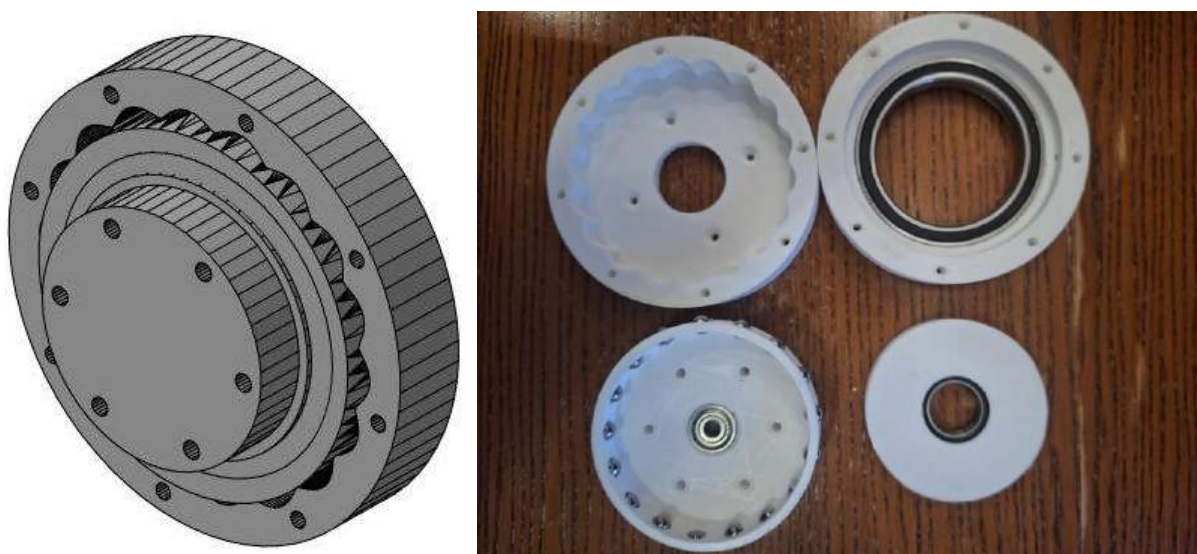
3D-модель и напечатанный вариант волнового редуктора
